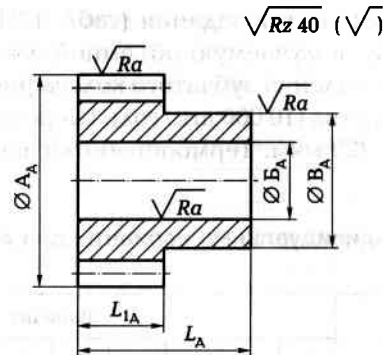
Эскиз обрабатываемого зубчатого колеса
